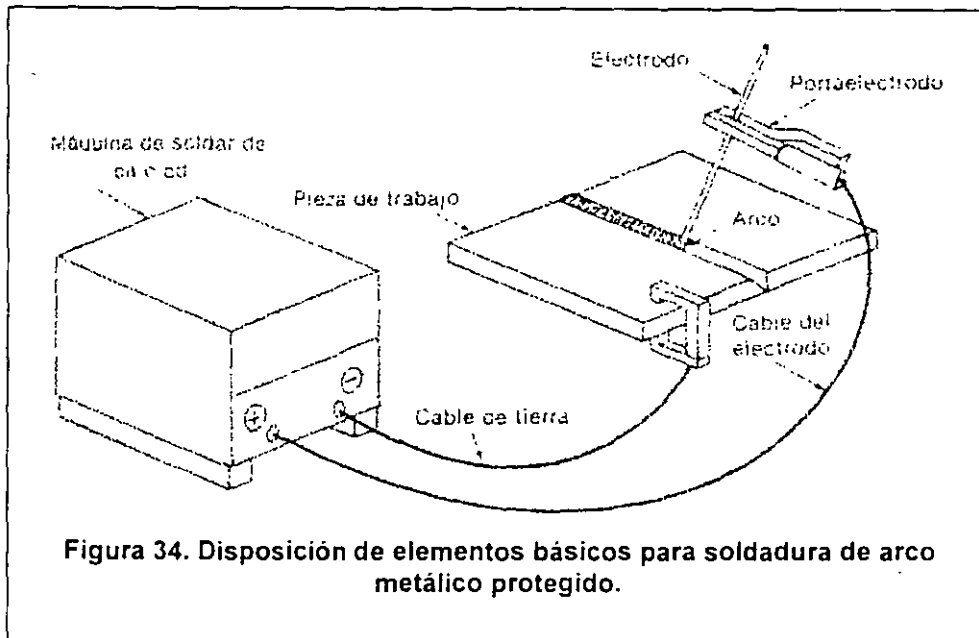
Disposición de elementos básicos para soldadura de arco metálico protegido.
